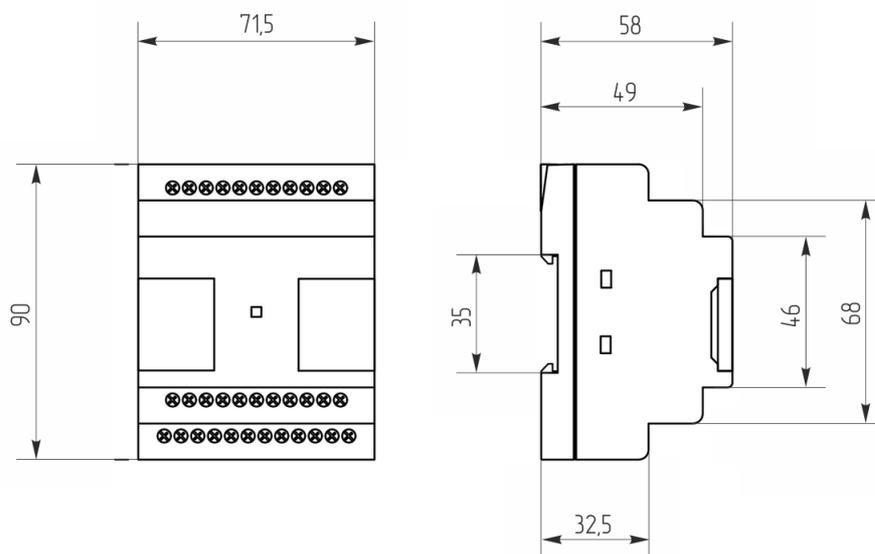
Габаритные и установочные размеры модуля расширения
